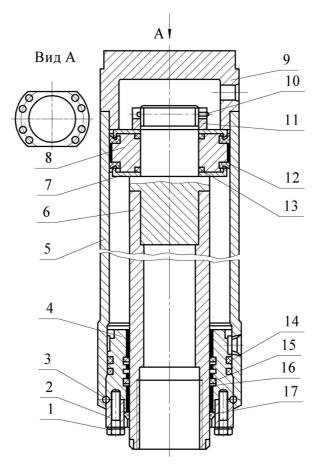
Гидроцилиндр подачи: 1 – болт; 2 – крышка; 3 – кольцо; 4 – передняя крышка; 5 – цилиндр; 6 – шток; 7 – кольцо; 8 – поршень; 9 – задняя крышка; 10 – стопорное кольцо; 11 – гайка; 12 – манжета; 13, 14 и 16 – кольцо; 15 – манжета; 17 – грязесъемник
